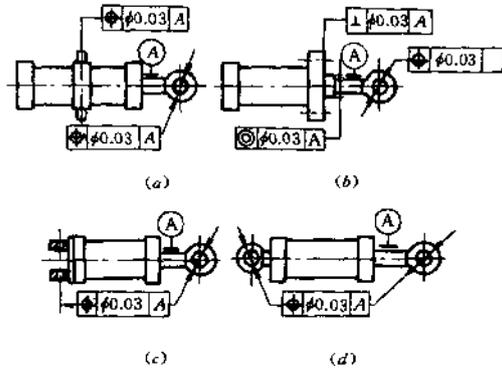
伺服液压缸安装尺寸的形位公差
